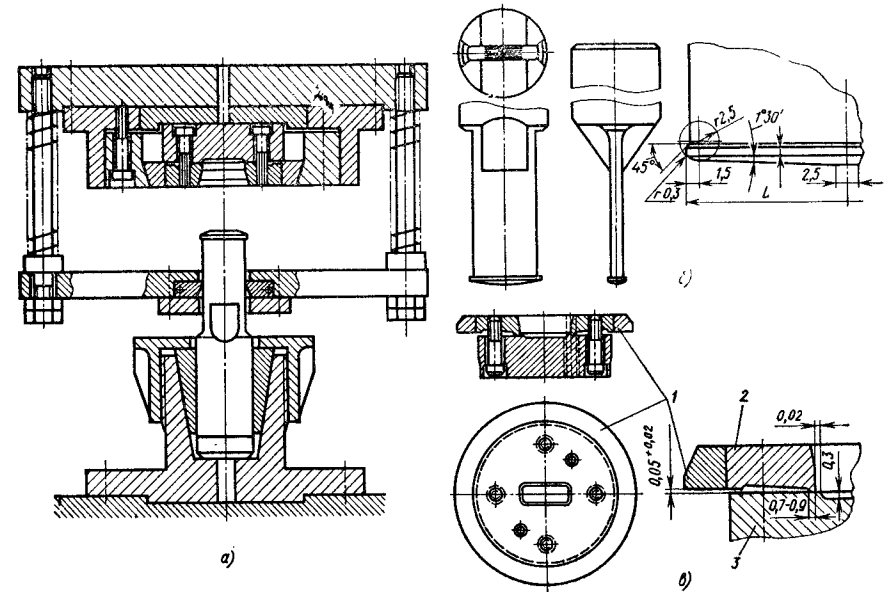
Штамп и рабочий инструмент для выдавливания коробчатых деталей: а — схема штампа для выдавливания; б — конструкция пуансона; в — конструкция матрицы; 1 — бандаж; 2 — верхняя часть матрицы; 3 — нижняя часть матрицы
